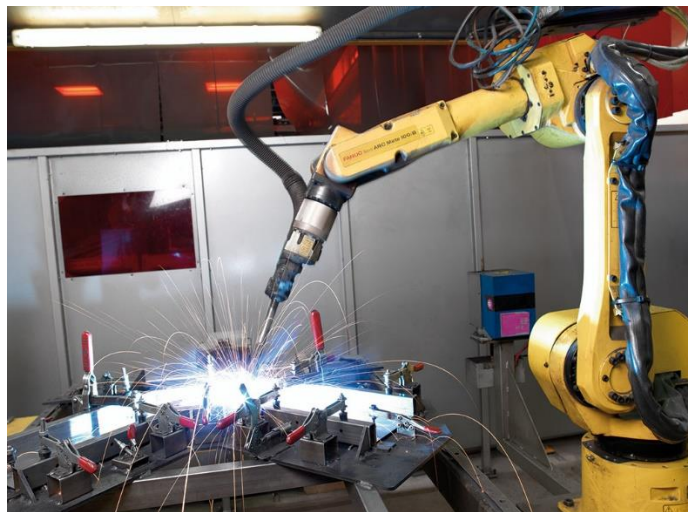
Exemplo de soldadura robotizada (Gasori, 2021)
